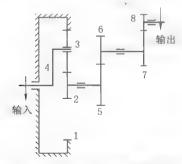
一级行星两级平行轴结构 1-内齿圈; 2-太阳轮; 3-行星轮; 4-行星架; 5-第二级大齿轮; 6-第二级小齿轮; 7-第三级大齿轮; 8-第三级小齿轮
